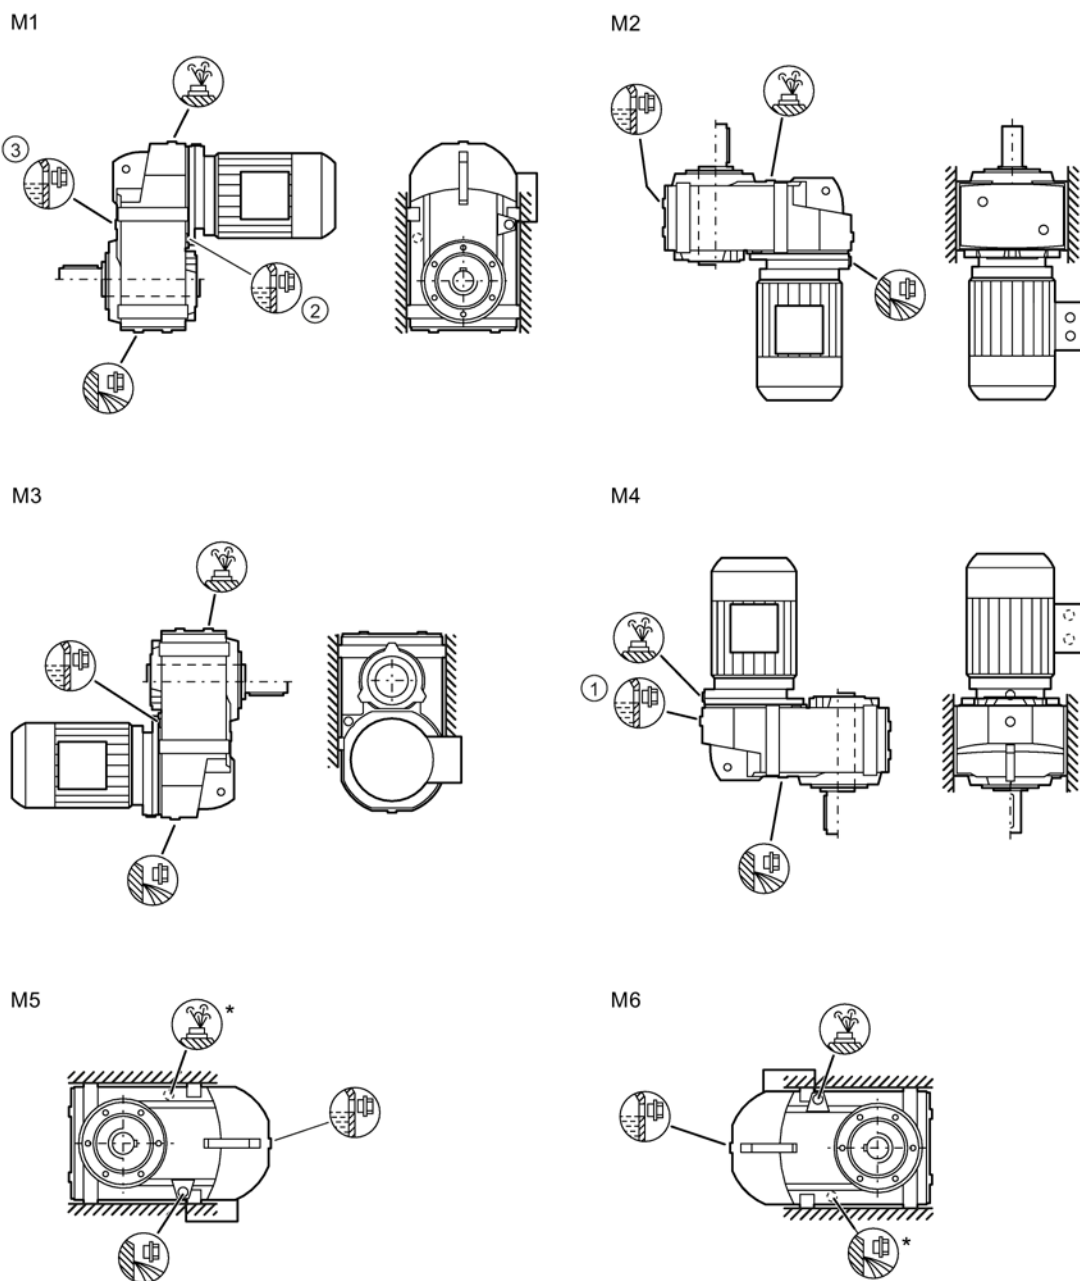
Монтажные положения для плоского редуктора F. в исполнении на лапах, типоразмеры 39-189
